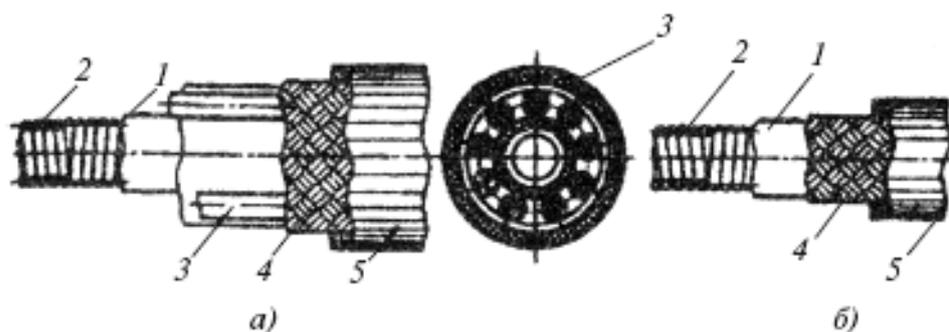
Конструкции гибких шлангов: а – типа КШПЭ; б – КМ; 1 – защитный слой; 2 – направляющий канал; 3 – провода цели управления; 4 – внутренняя защитная оболочка; 5 – наружный защитный слой
